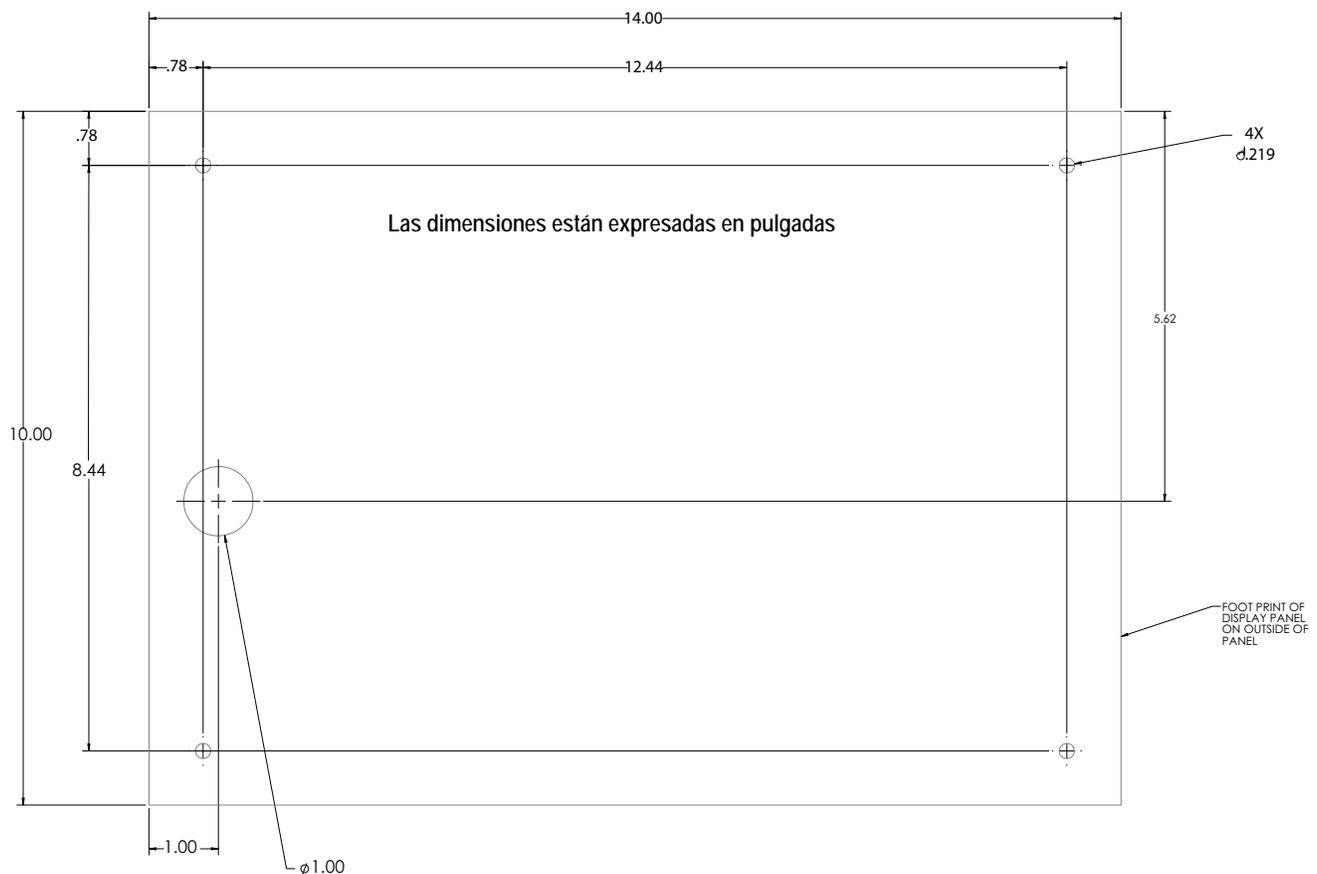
Dimensiones del montaje en panel de 12 pulgadas solo táctil
